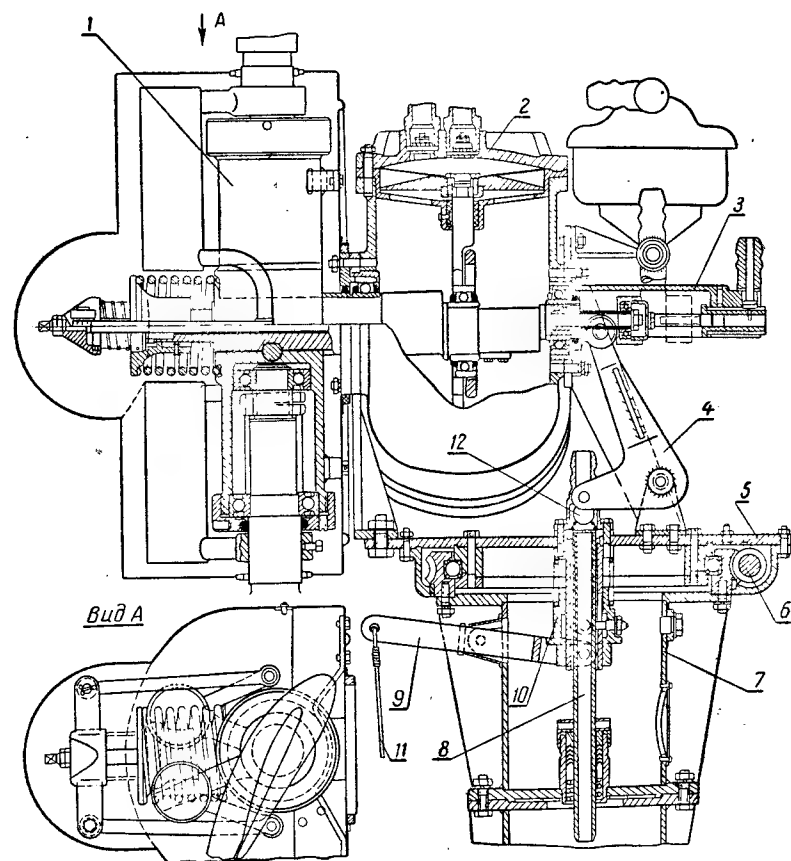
Головка агрегата «Вихрь» (ВНП-4М):
